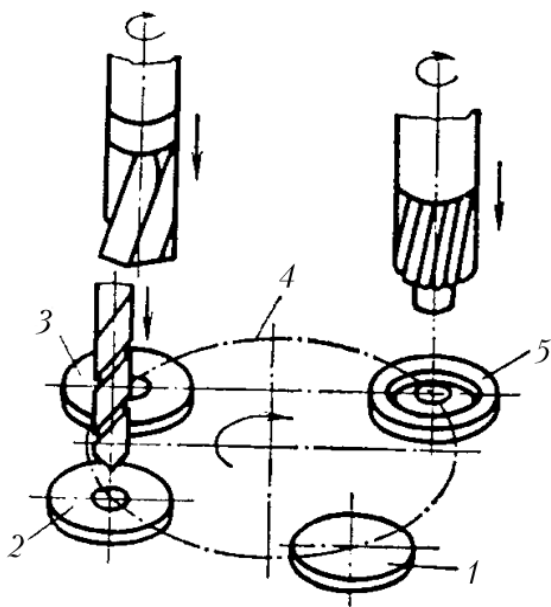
Чотирипозиційна обробка деталі на тришпиндельному верстаті: 1 – встановлення і знімання деталі; 2 – свердління; 3 – зенкування; 4 – стіл; 5 – зенкування.
